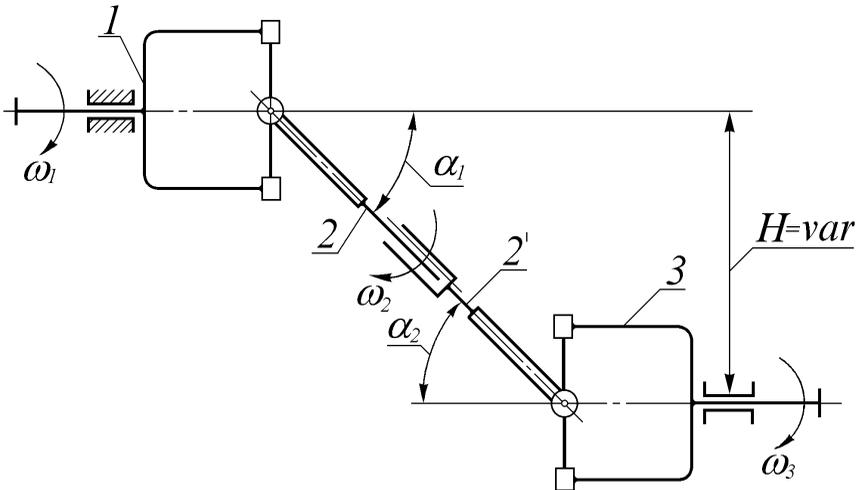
Кінематична схема здвоеного шарніра Гука
